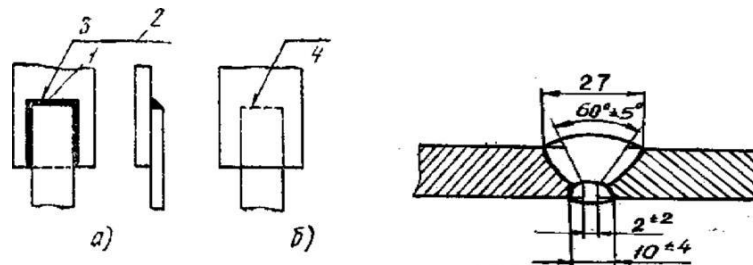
Условное изображение сварных швов:
